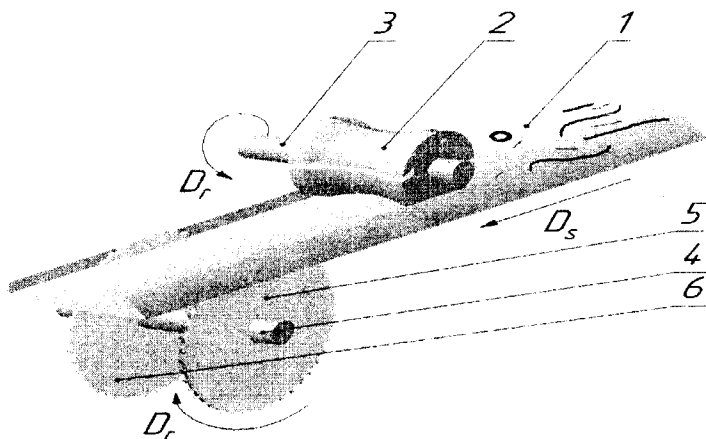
Схема обработки горбыля: D_r – направление главного движения инструментов, D_s – направление движения подачи заготовки
